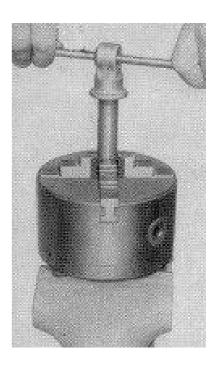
Kolbenstange ins Dreibackenfutter spannen
